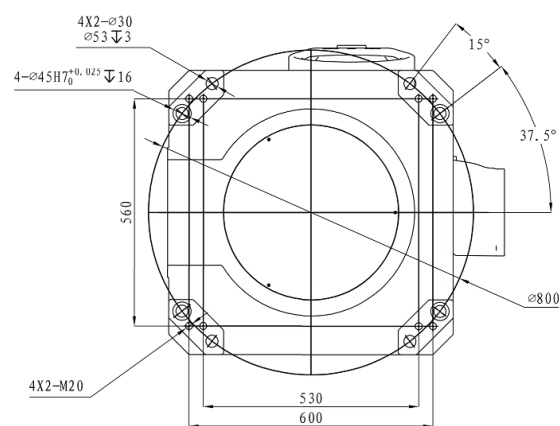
Габаритные чертежи робота-манипулятора SR50-2180.
